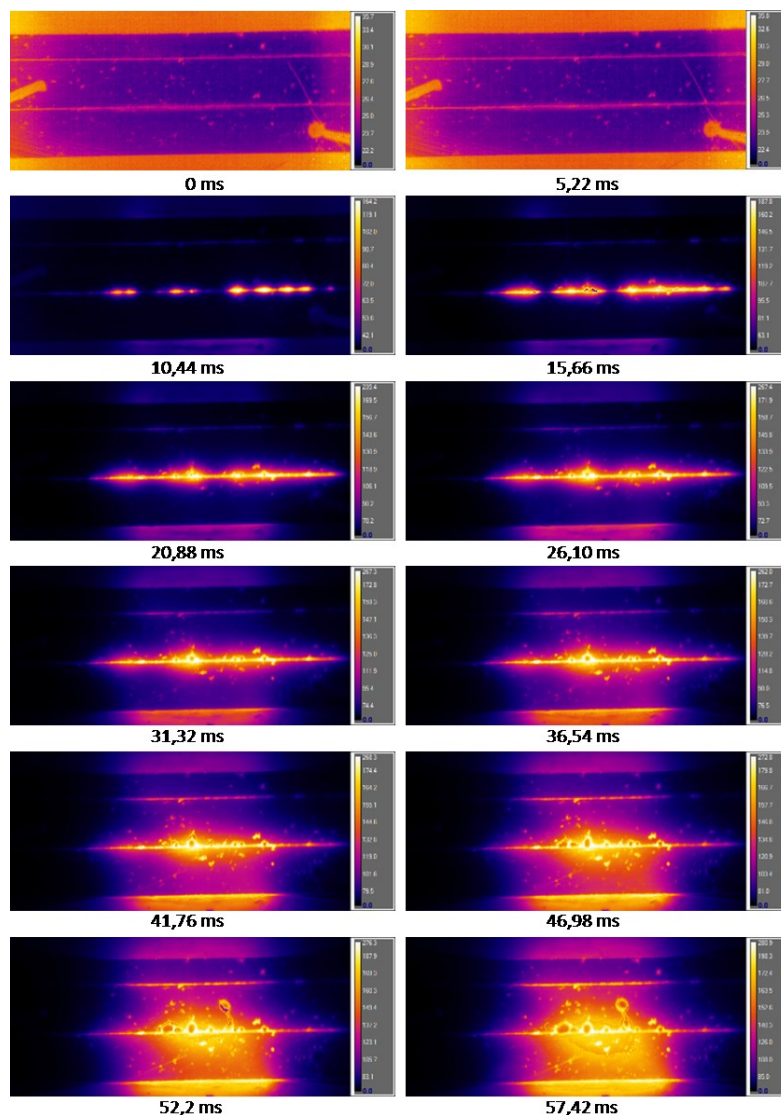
Séquence de thermogrammes lors du soudage d'un demi-point de l'assemblage dissymétrique AM-DP-DP.
